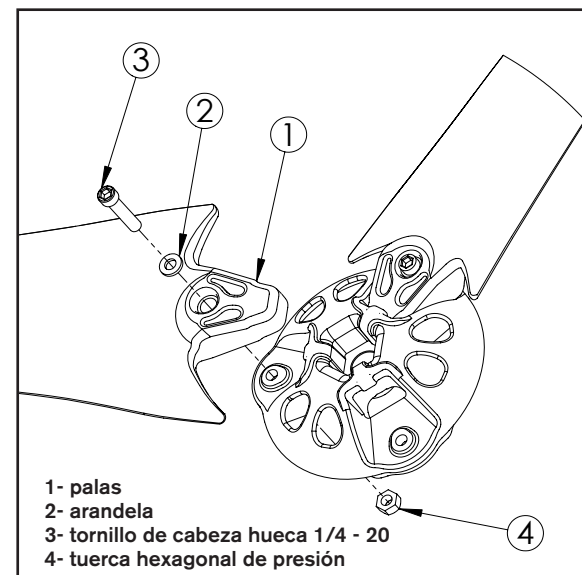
detalle de la fijación de las palas del Air Breeze
